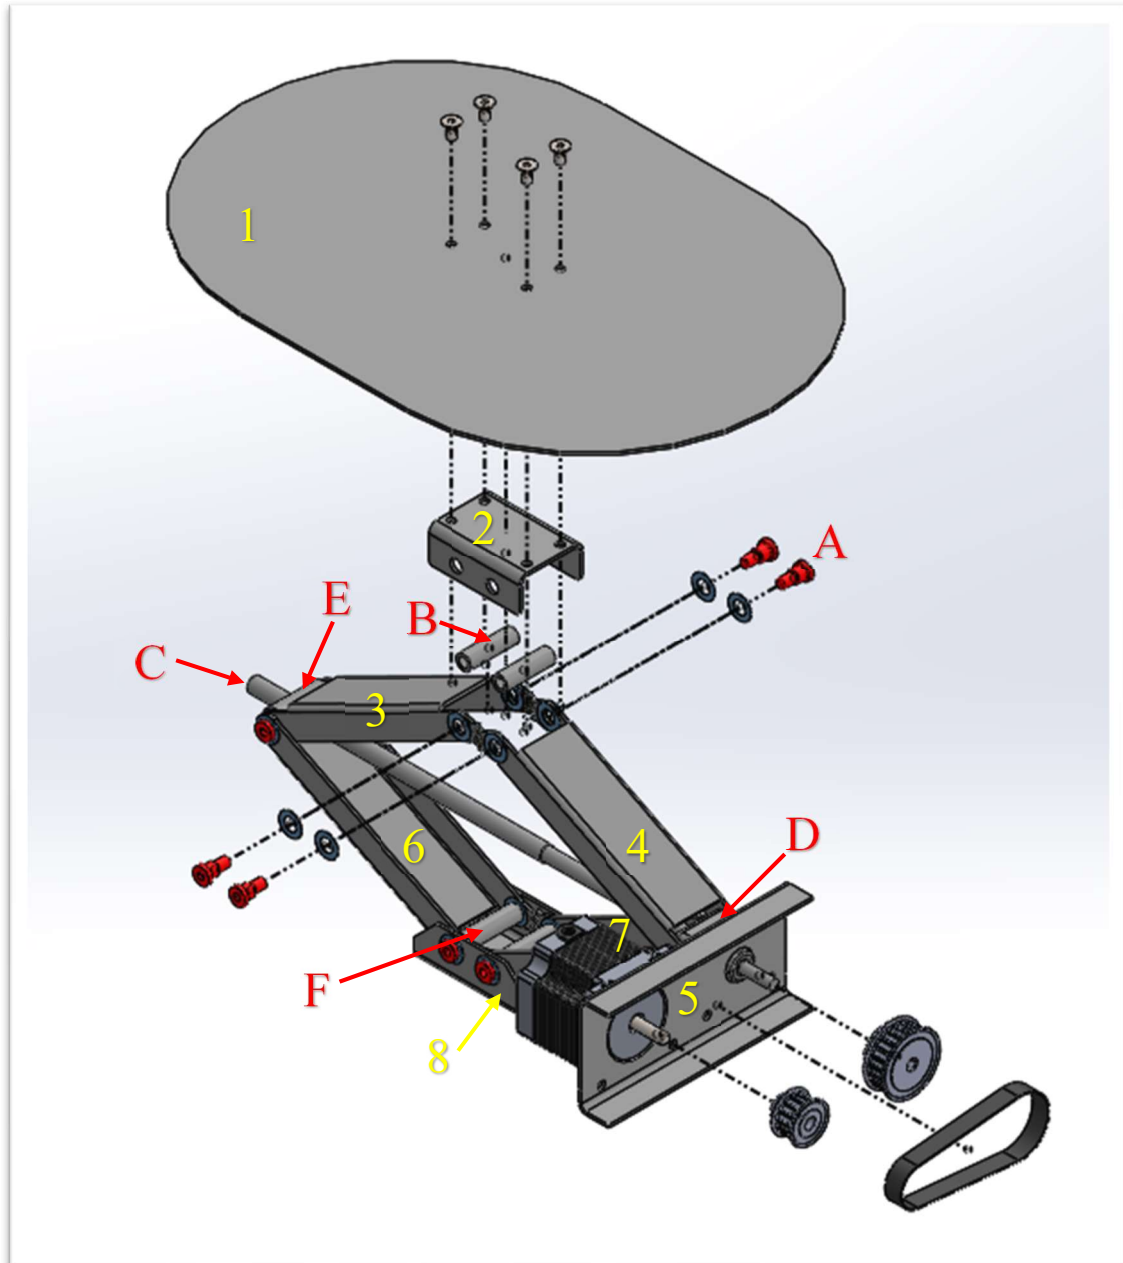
Piezas Elevador mecánico. Fuente: Elaboración propia
